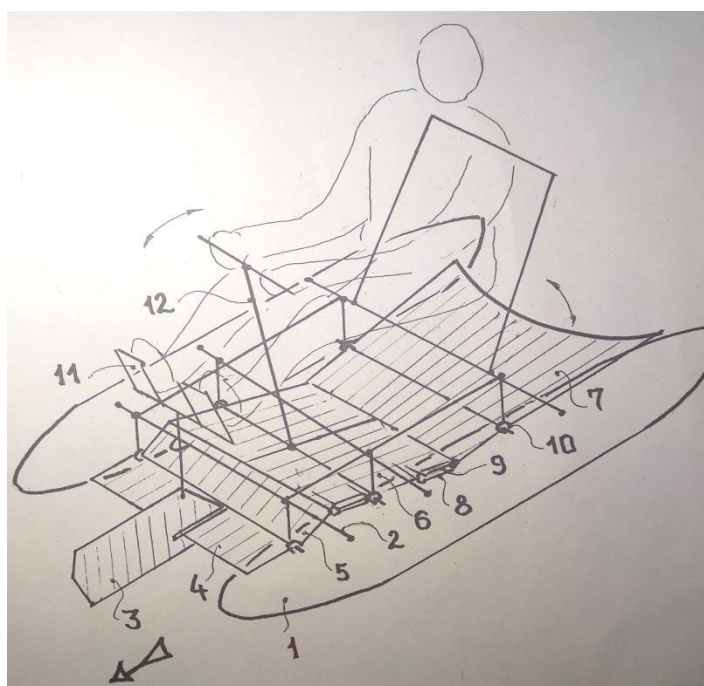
Схема катамарана: 1 – корпус; 2 – рама; 3 – руль; 4 – неподвижная площадка; 5 – поворотная лопасть; 6 – рабочая лопасть; 7 – гребущая лопасть; 8 – паз; 9 – отклоняющийся закрывок; 10 – подшипник; 11 – педаль; 12 – рычаг.
